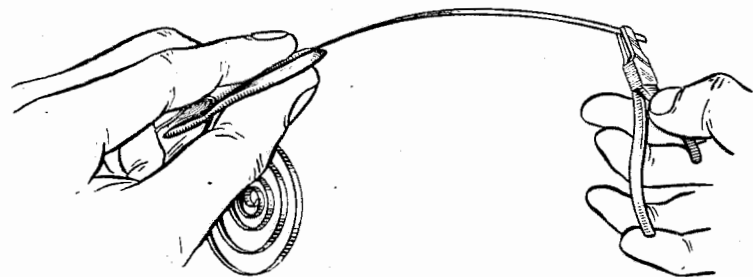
Приспособление для установки пружины в барабан английской конструкции.
